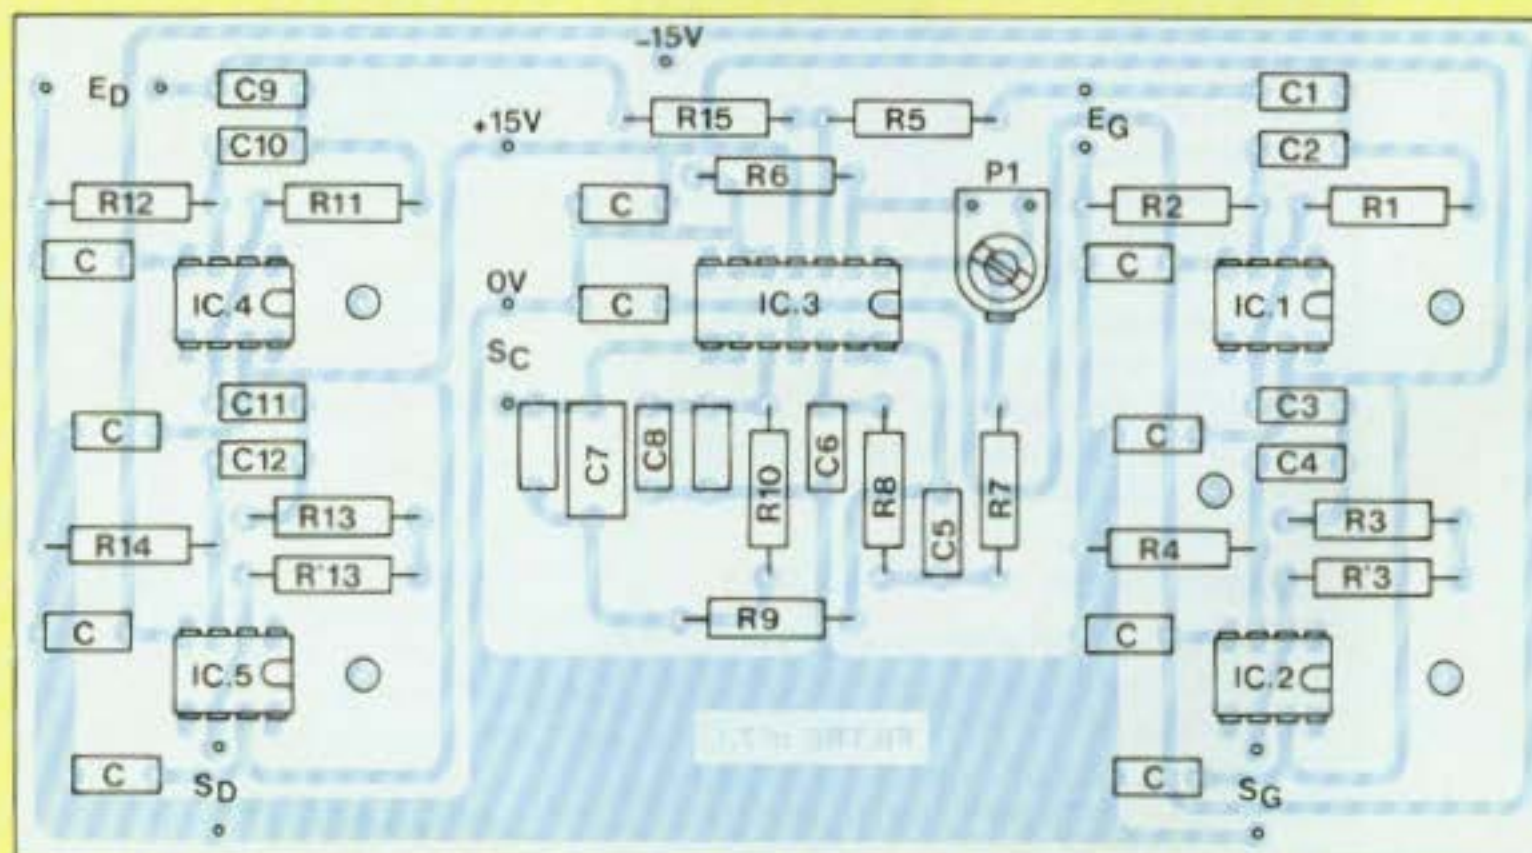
Le plan de câblage du filtre actif est suffisamment précis pour éviter toute erreur.
